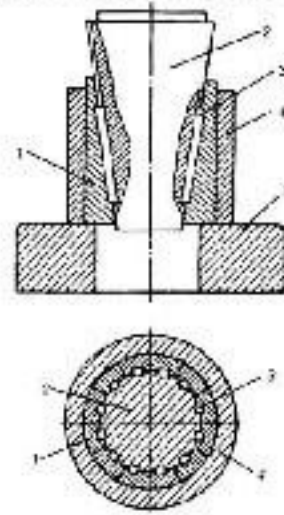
Схема приспособления для раздачи втулки: 1 — клин-сектор; 2 — пуансон; 3 — направляющая шпонка; 4 — деформируемая втулка; 5 — плита
